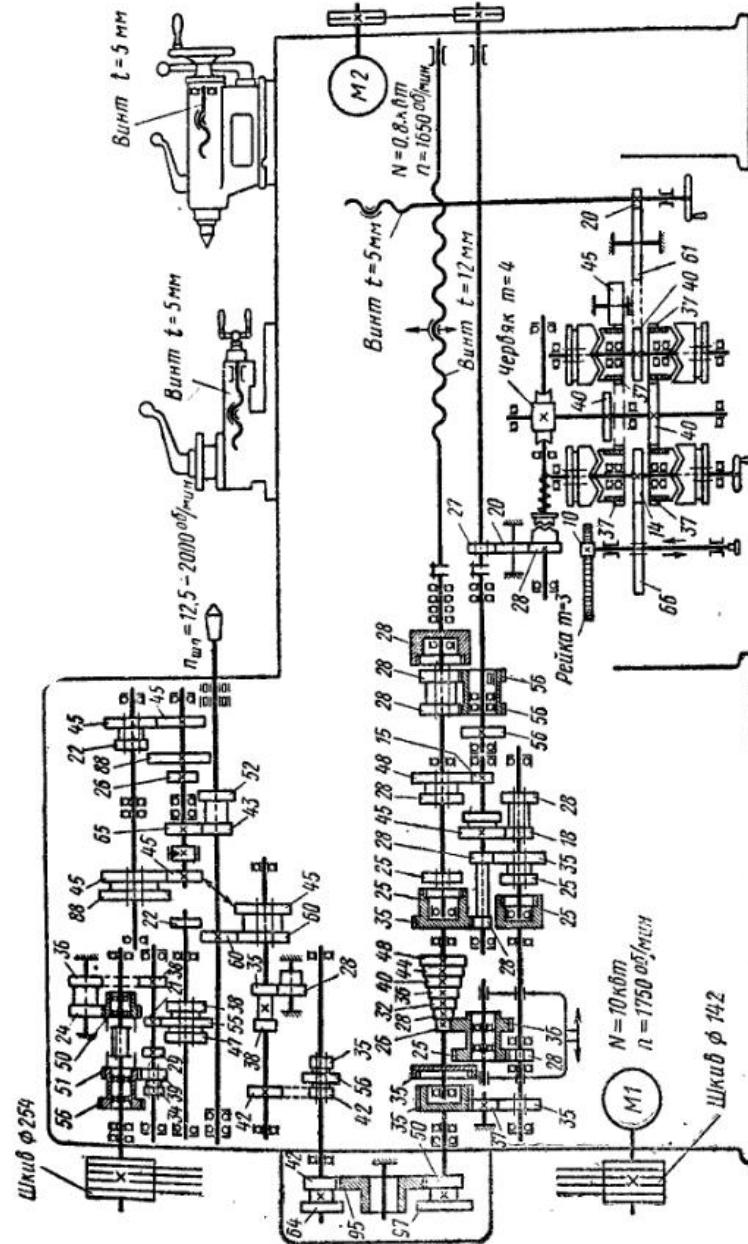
Кинематическая схема токарно-винторезного станка 1К62 (цифрами обозначены числа зубьев колес)
